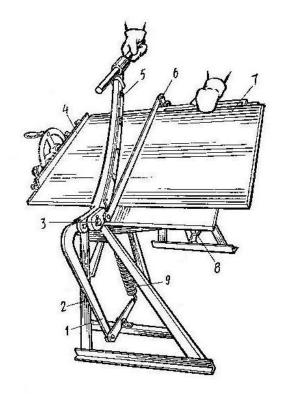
Резка металлического листа ручными маховыми (рычажными) пожницами: I— рычажный механизм. 2— стойка, 3— осъвращения вожа, 4— упор, 5— нож, 6— лрнжим, 7— лист металла, 8— педаль, 9— пружина
